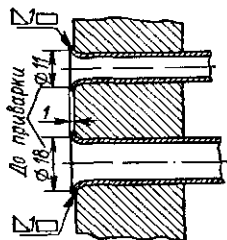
Конструкция, соединения трубок с трубными досками (перед сваркой).
